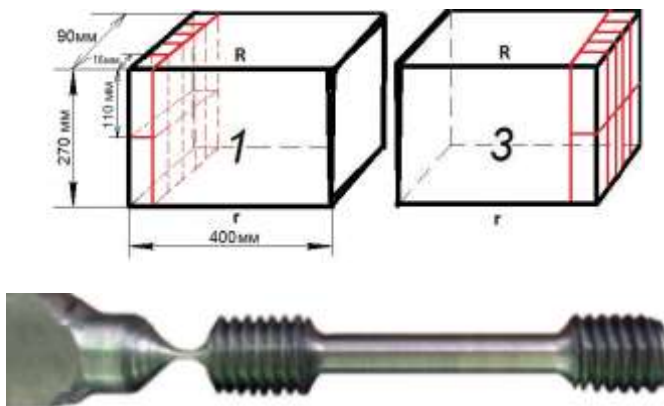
Схема вырезки образцов из темплетов слябовой непрерывно-литой заготовки и вид подготовленного образца
